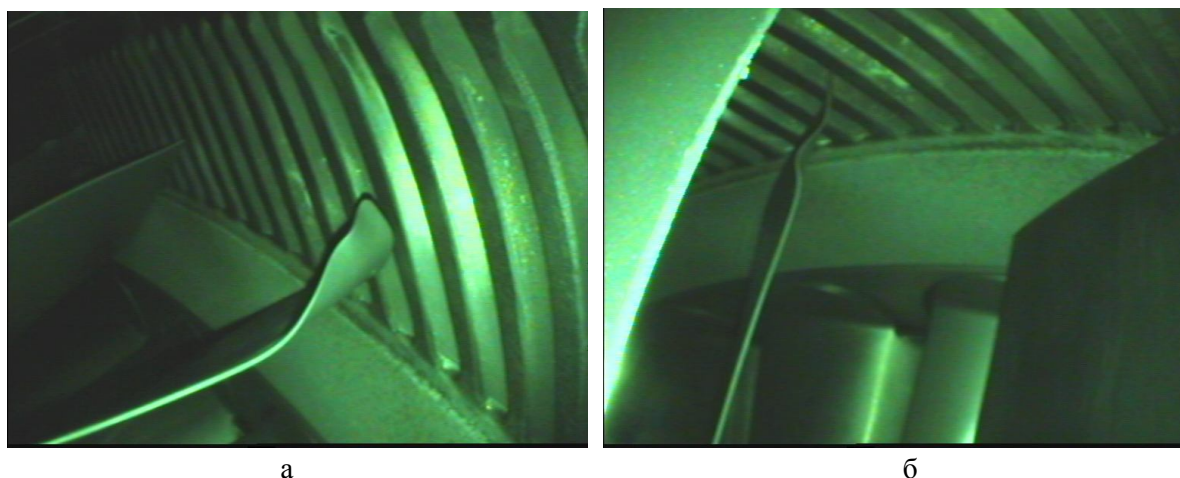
Фрагмент бороскопического обследования компрессора промежуточного давления двигателя RB211-535E4 (а — лопатка компрессора № 23, б — лопатка компрессора № 31)
